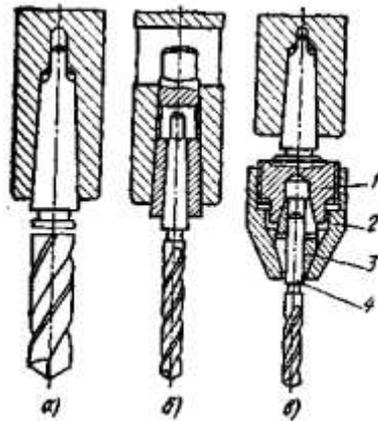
Схемы закрепления инструмента в шпинделе станка
